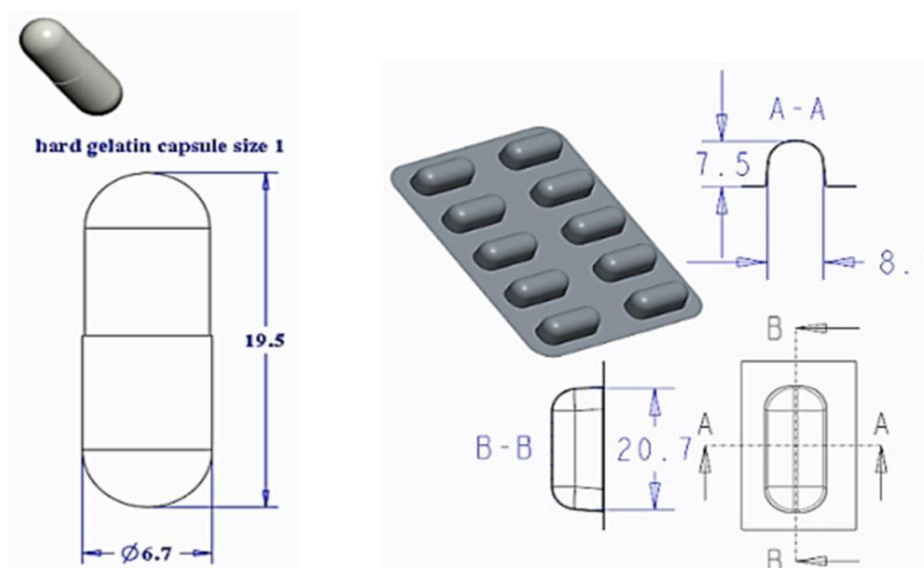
Figure 4-15 placebo capsules and blister - dimensions
